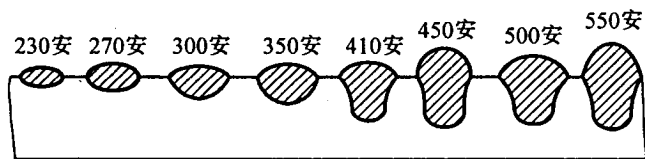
焊接电流对焊缝成形的影响
